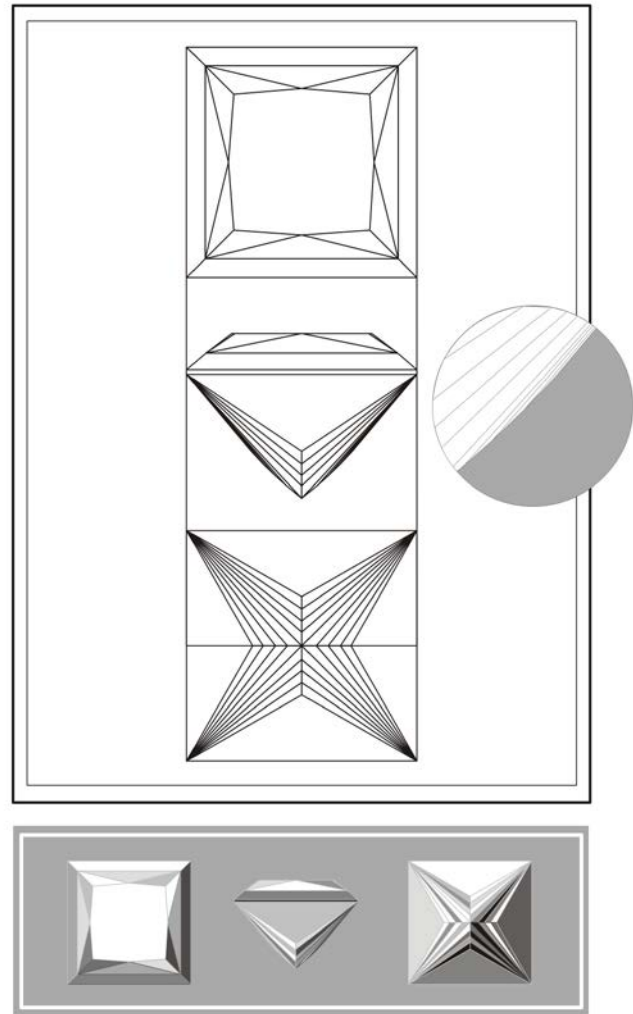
Technisches Zeichnen – Schmuckdiamantschleifer – Princess Cut © Schäfer
